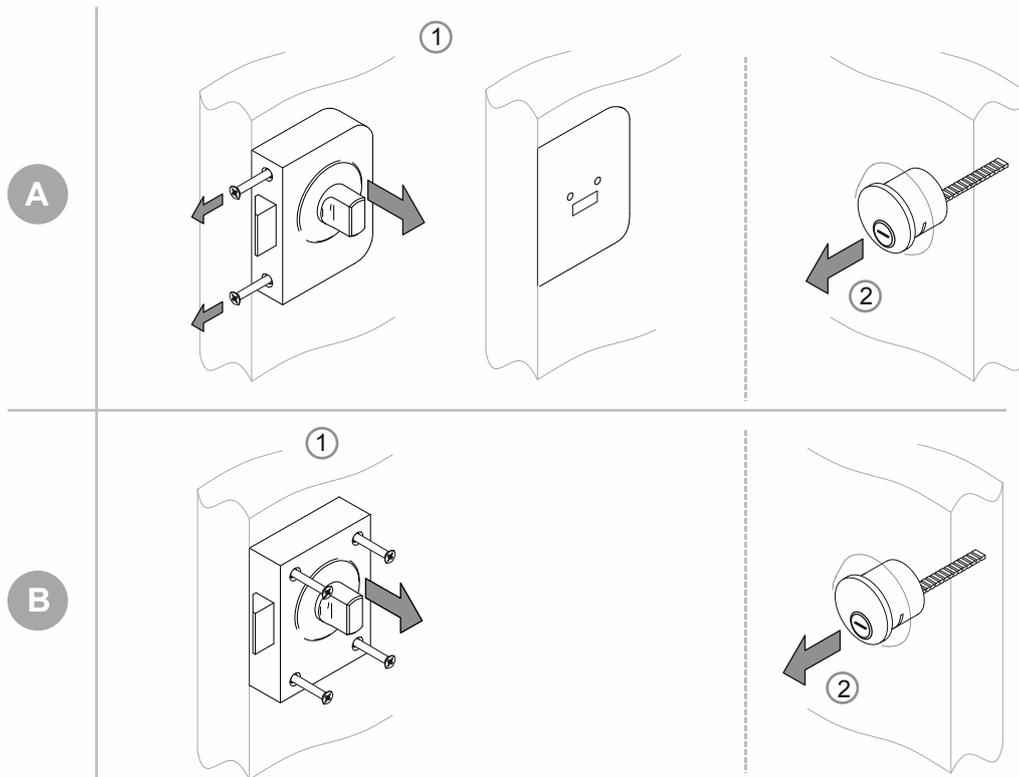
Демонтаж старого цилиндра: профиль RIM
